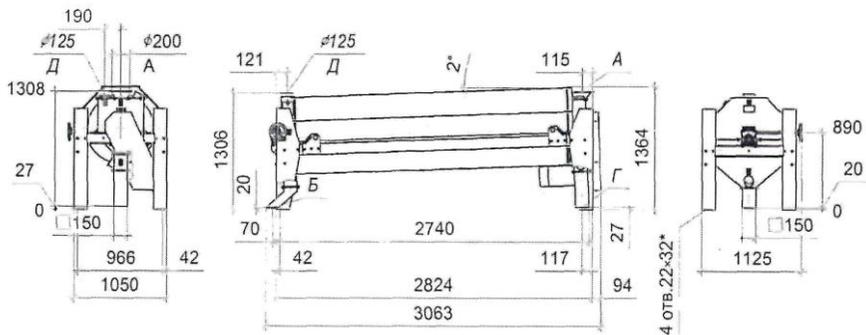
Установочные и присоединительные размеры триеров цилиндрических ТБ-70, ТК-70
